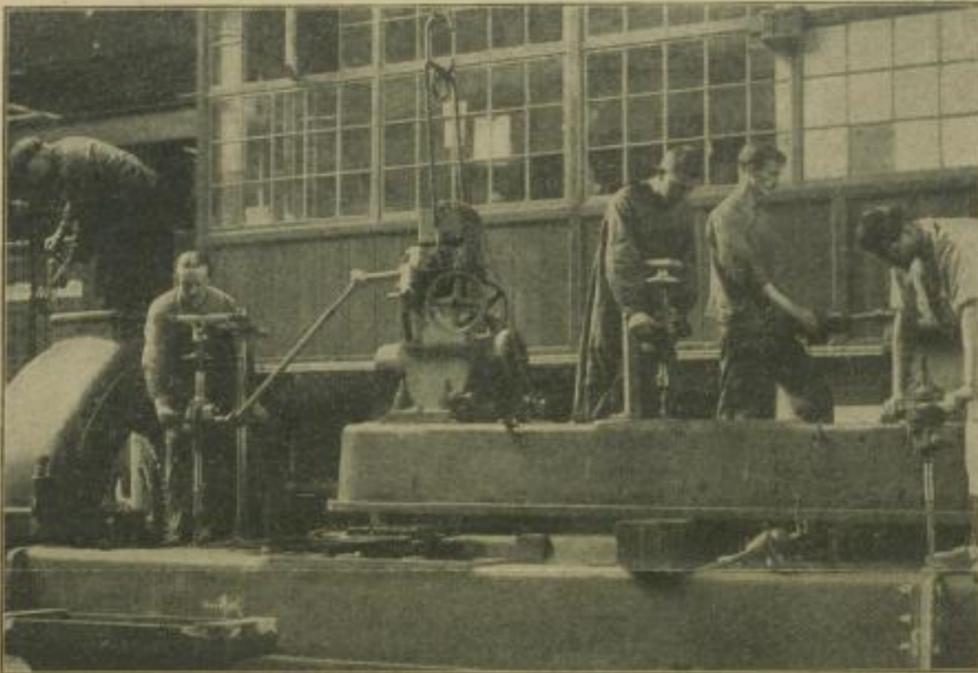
Bearbeitung schwerer Gussstücke durch fahrbare und Hand-Bohrmaschinen, Gewindeschneidmaschinen und Aufreibmaschinen
